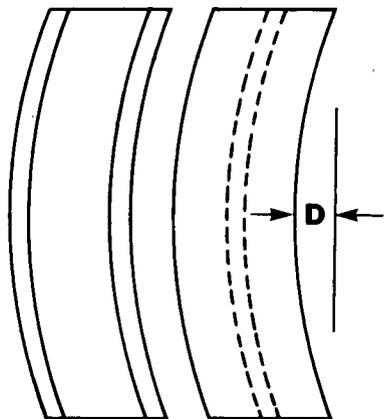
RELATION ENTRE L'ÉPAISSEUR D'UN JOINT SOUDÉ, LA DIMENSION DES DÉFAUTS ET LEUR FRÉQUENCE
